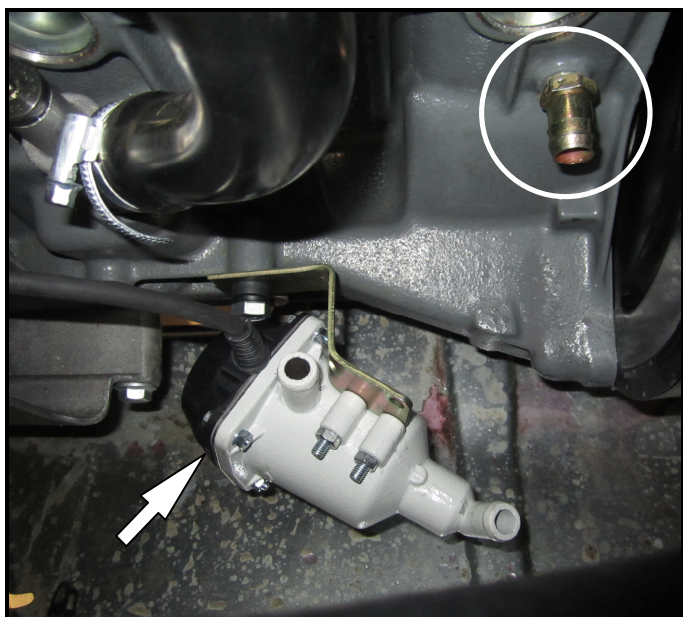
Монтаж кронштейна на подогревателе, болт крепления и монтаж штуцера
